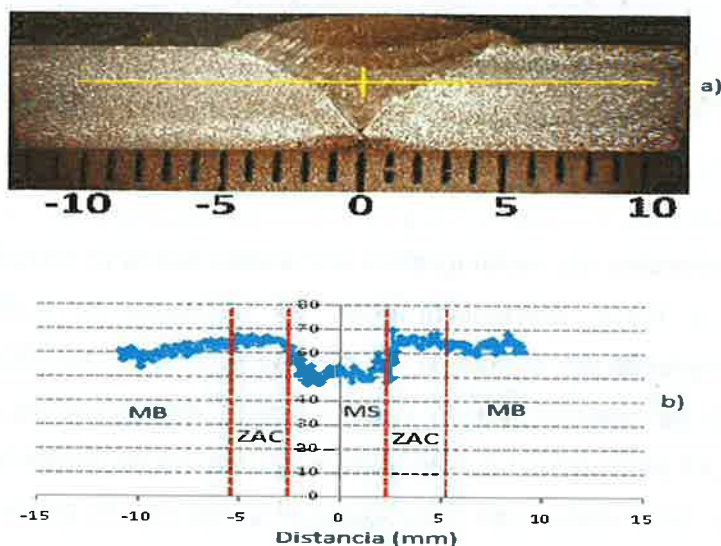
Perfil de microindentación de la union soldada TIG.
